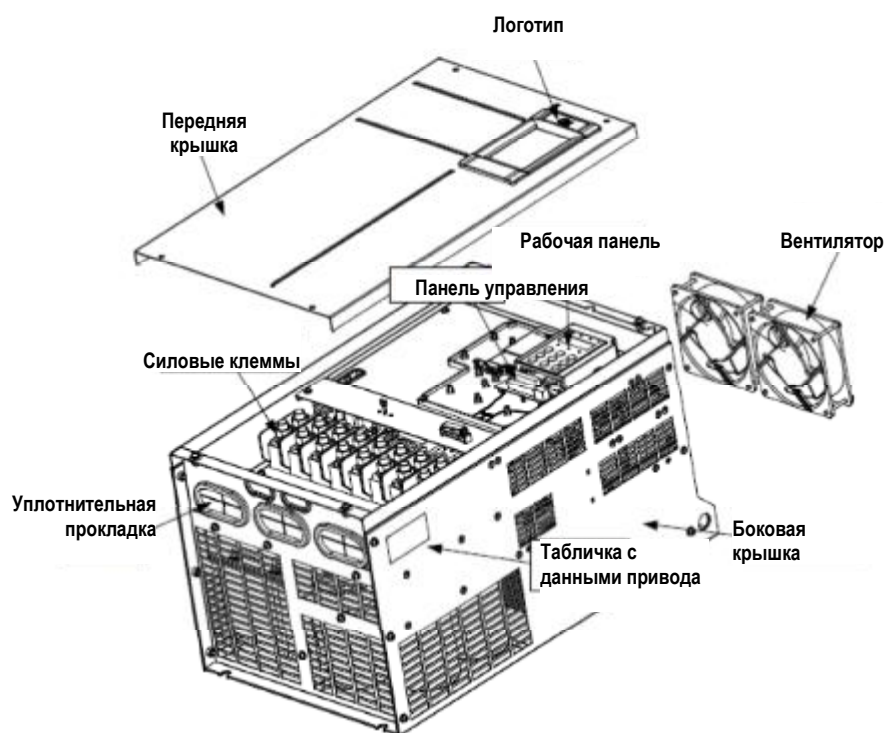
Компоненты MD290 для металлического корпуса (трехфазный ток 380 – 480 В, от 45G/55P до 110G/132P).
